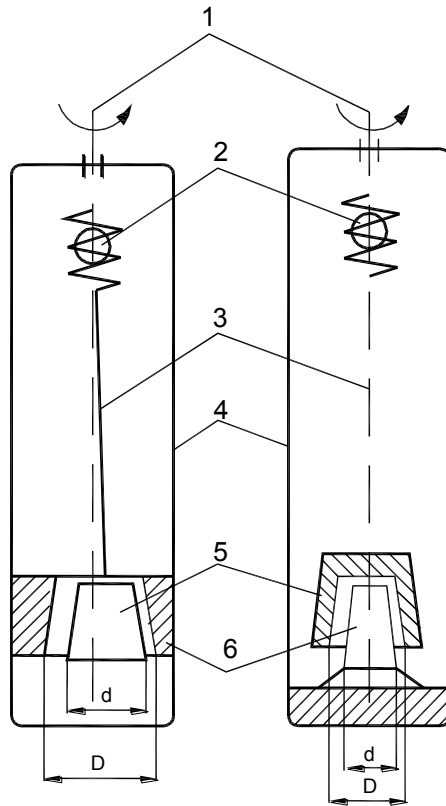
Конструктивная схема глубинного вибровозбудителя
